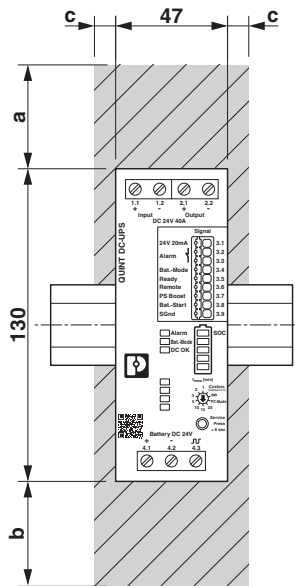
Geräteabmessungen und minimale Sperrflächen (Maße in mm)
